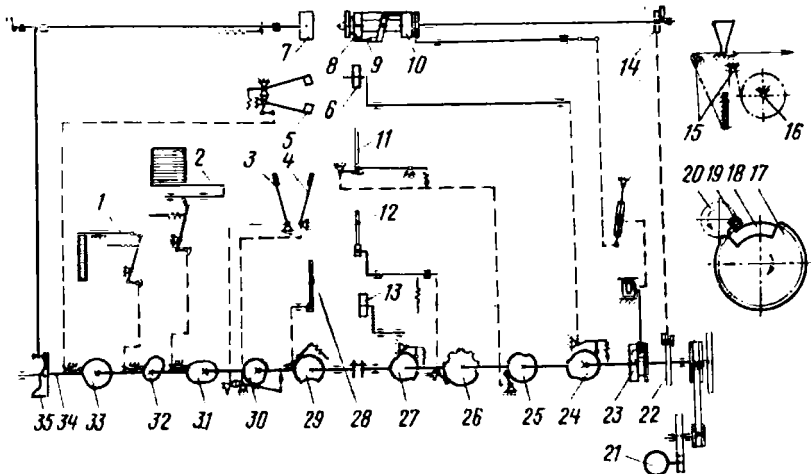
Кинематическая схема коробкоклепального станка СпКВ-3А:
